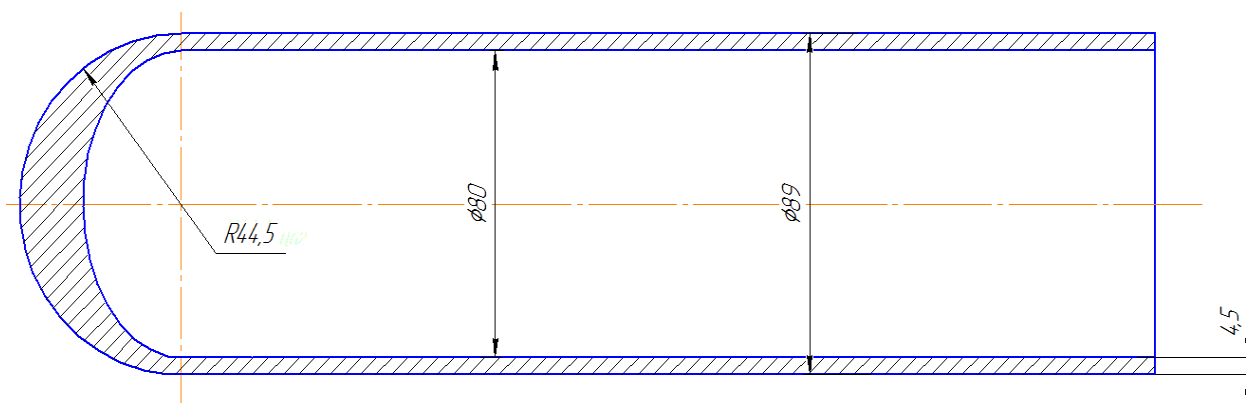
Ескіз трубної заготовки з днищем, отриманого шляхом обкатування трубної заготовки ІТ
